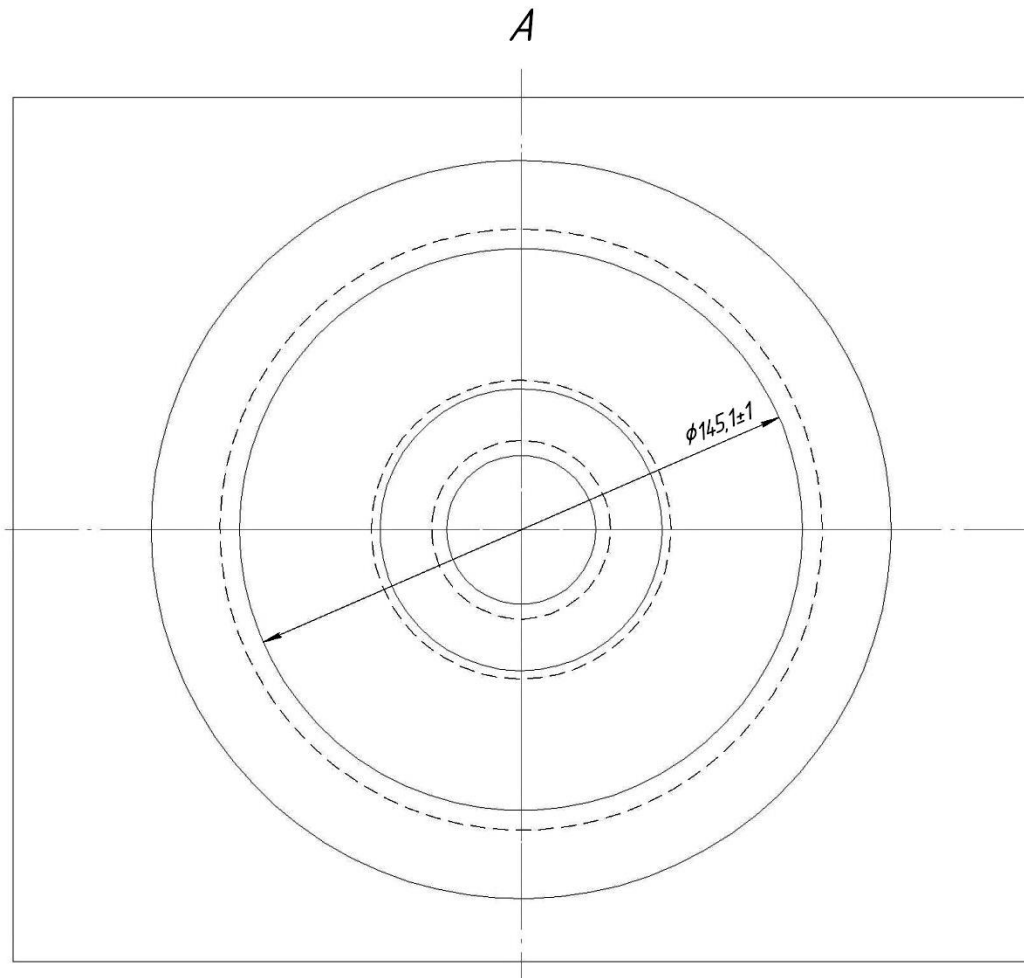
Ескіз заготовки (деталі «Корпус И-042.8.H72.00)
